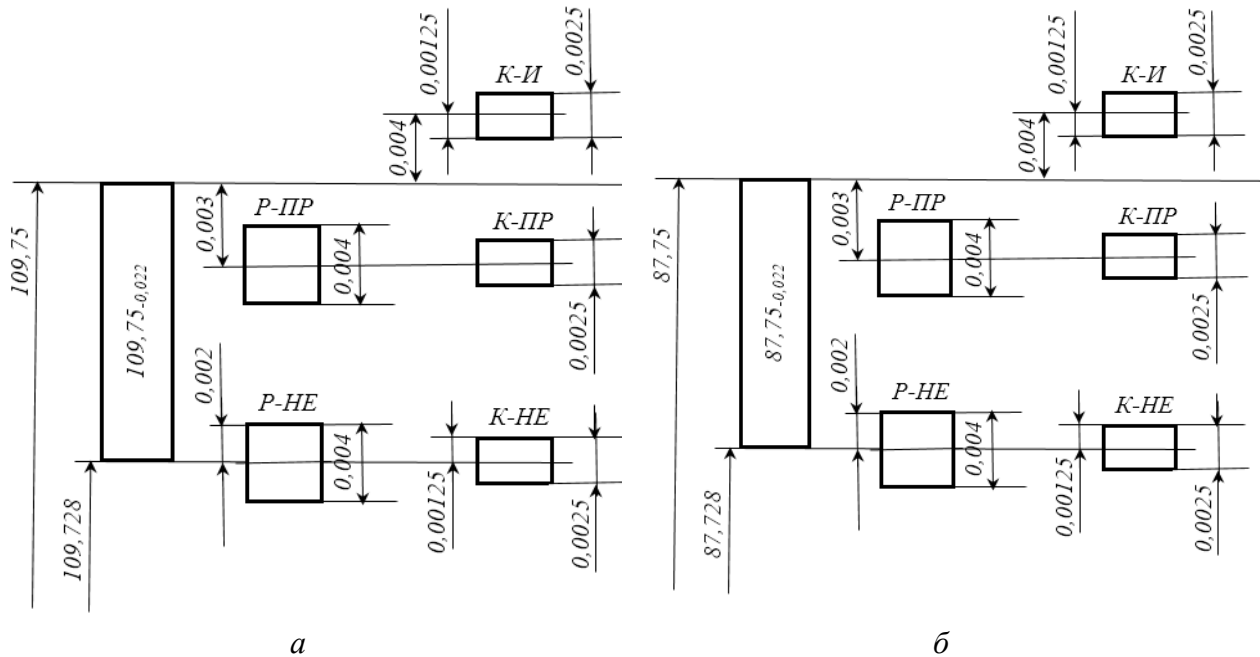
Схема расположения полей допусков калибра-скобы для контроля размера шейки коленчатого вала двигателей ЯМЗ после шлифовки под ремонтный размер: а) коренной; б) шатунной
